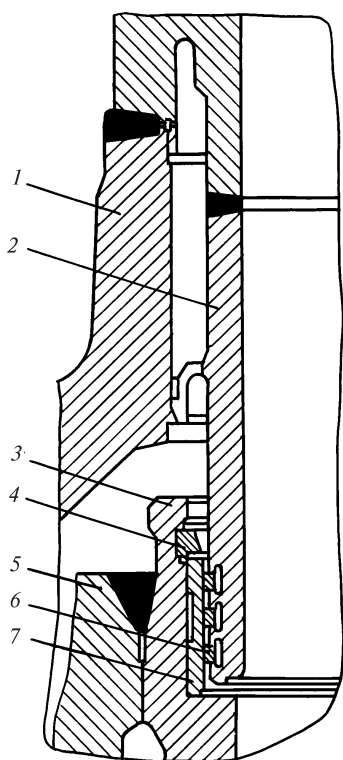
Конструкция паровпуска двухстенного ЦВД
